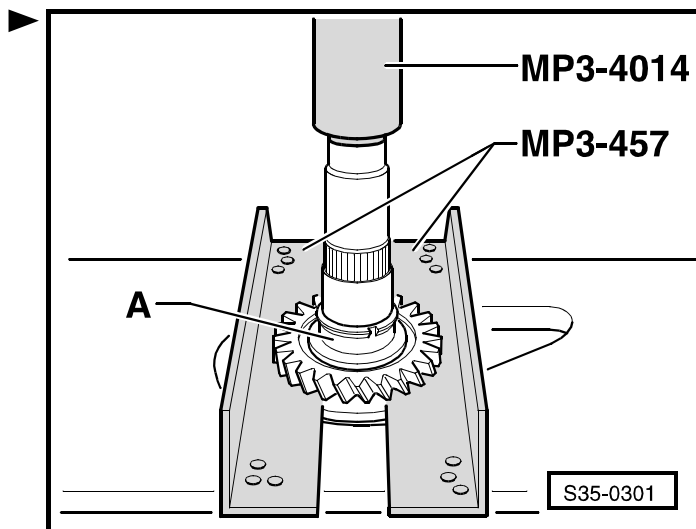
Выпрессовывание каретки синхронизатора для передачи заднего хода
